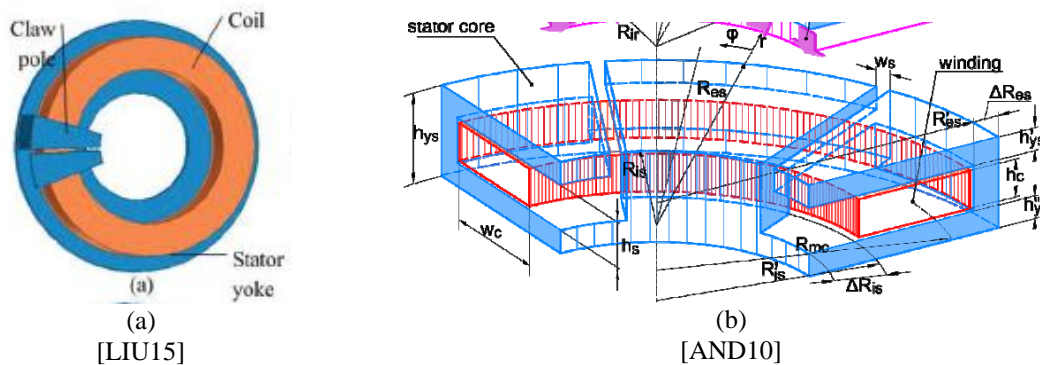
Machines à griffes à flux axial : (a) [LIU15] (b) [AND10]
